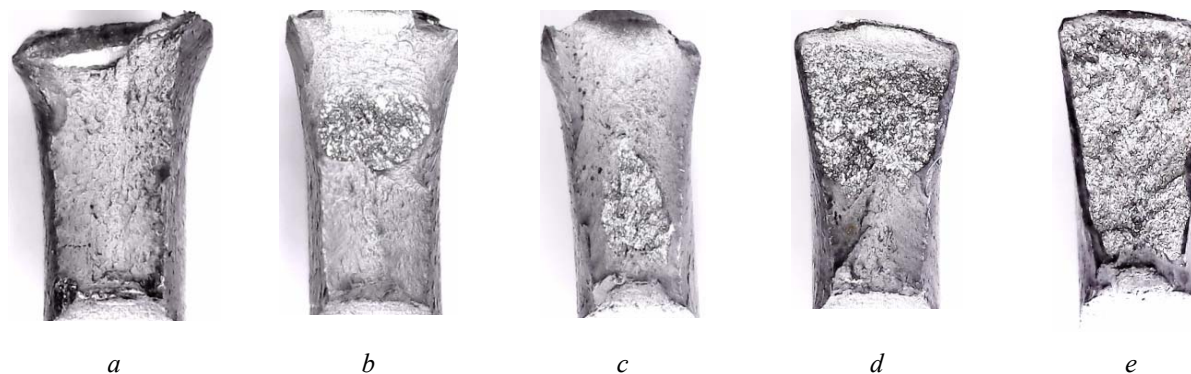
Общий вид излома образцов, испытанных на ударный изгиб (вырезанных вдоль направления наплавки) при температурах: +20 °C (a); 0 °C (b); -20 °C (c); -40 °C (d); -60 °C (e)
